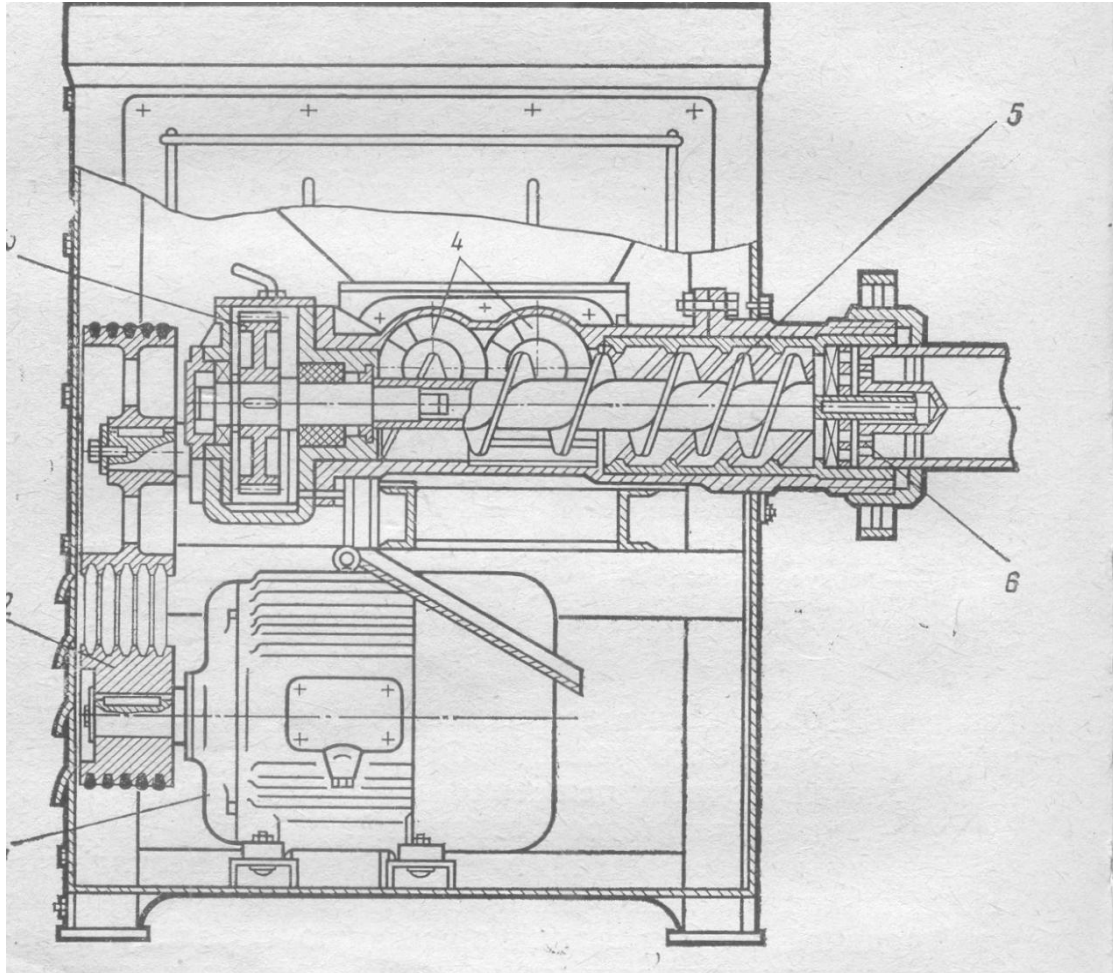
Вовчок К6-ФВЗП-200. 1 – електродвигун; 2 – клинопасова передача; 3 – редуктор; 4 – живильні шнеки; 5 – робочий шнек; 6 – подрібнюючий механізм.
